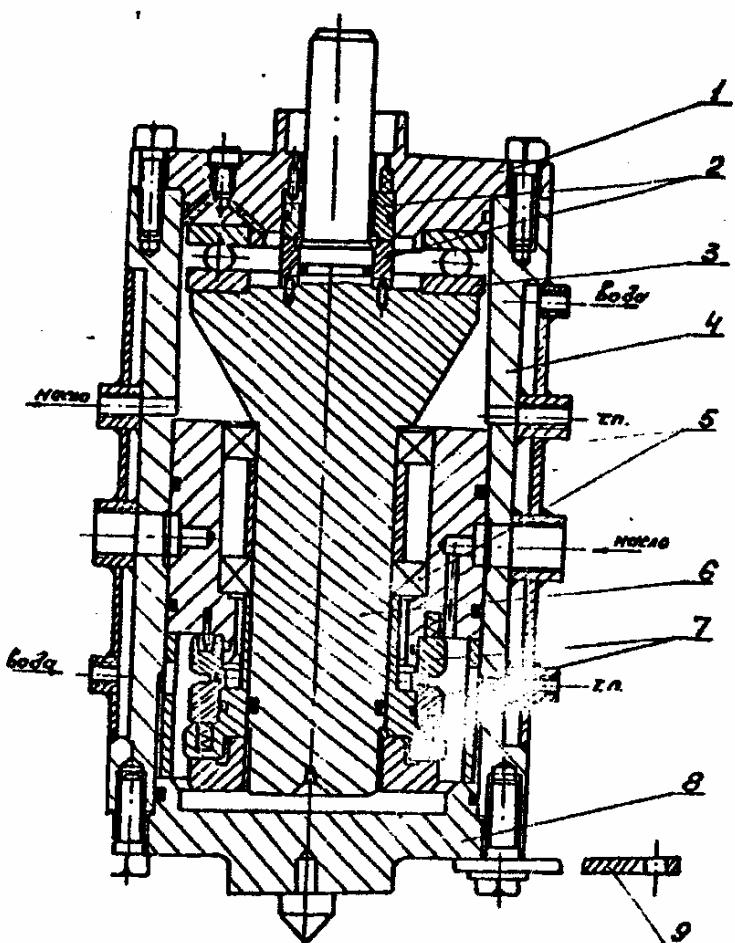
Рабочий узел стенда для испытания торцевого уплотнения: 1 – верхняя крышка; 2 – запирающее торцовое уплотнение; 3 – шарикоподшипник; 4 – корпус; 5 – шарикоподшипник; 6 – вал; 7 – торцовое уплотнение; 8 – нижняя крышка; 9 – рычаг.
